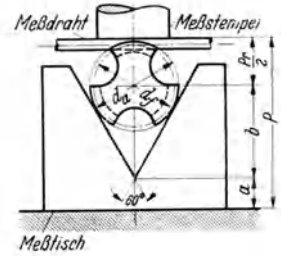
Messen des Flankendurchmessers dreiteiliger Gewindebohrer.
